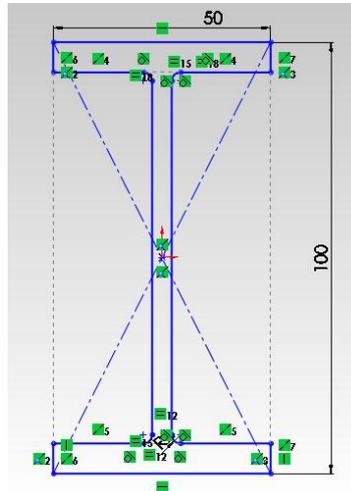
Geometría de perfil IPE para travesaños.⁷⁶
